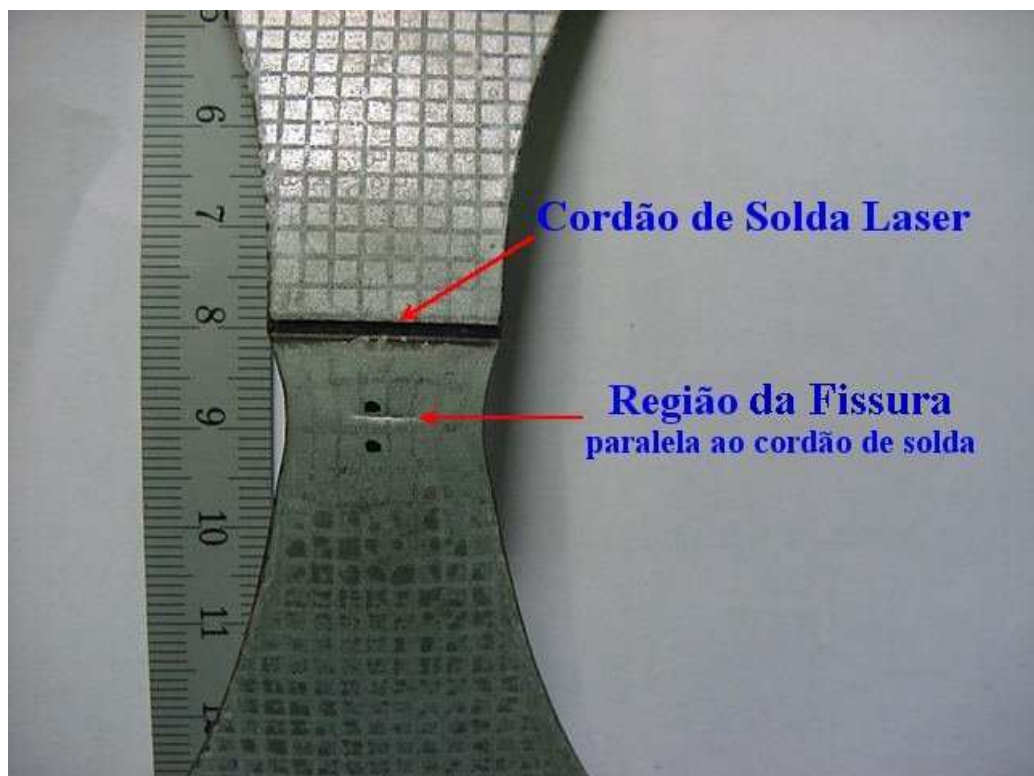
Tipo de fissura nos corpos de prova do ensaio Nakajima modificado.
